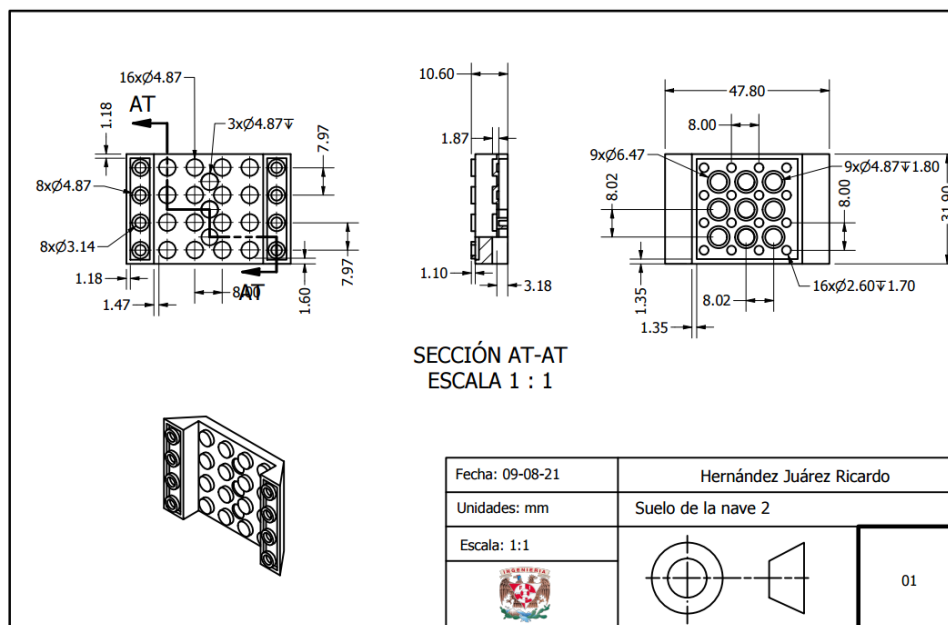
Plano técnico de pieza en Nave Espacial LEGO.
